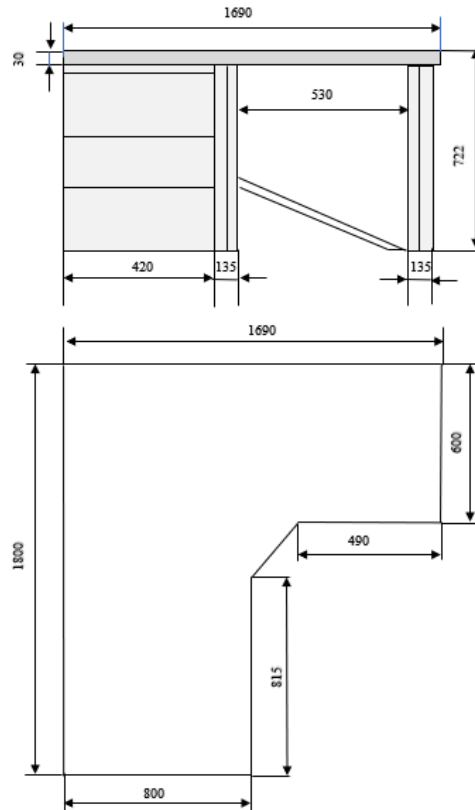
Croquis puesto de trabajo trabajador 2. Fuente: elaboración propia
